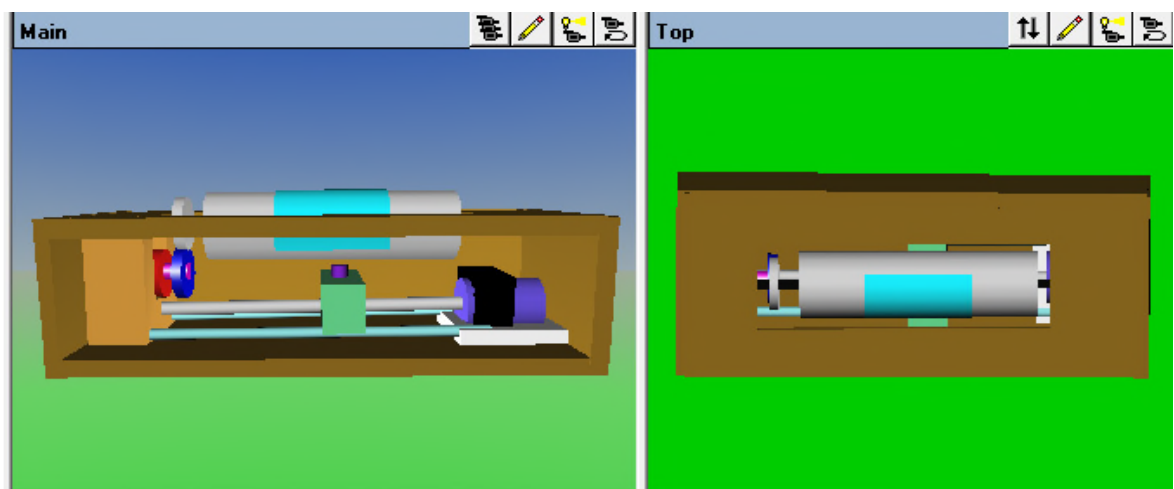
Mécanisme d'engrenage et vis sans fin.
